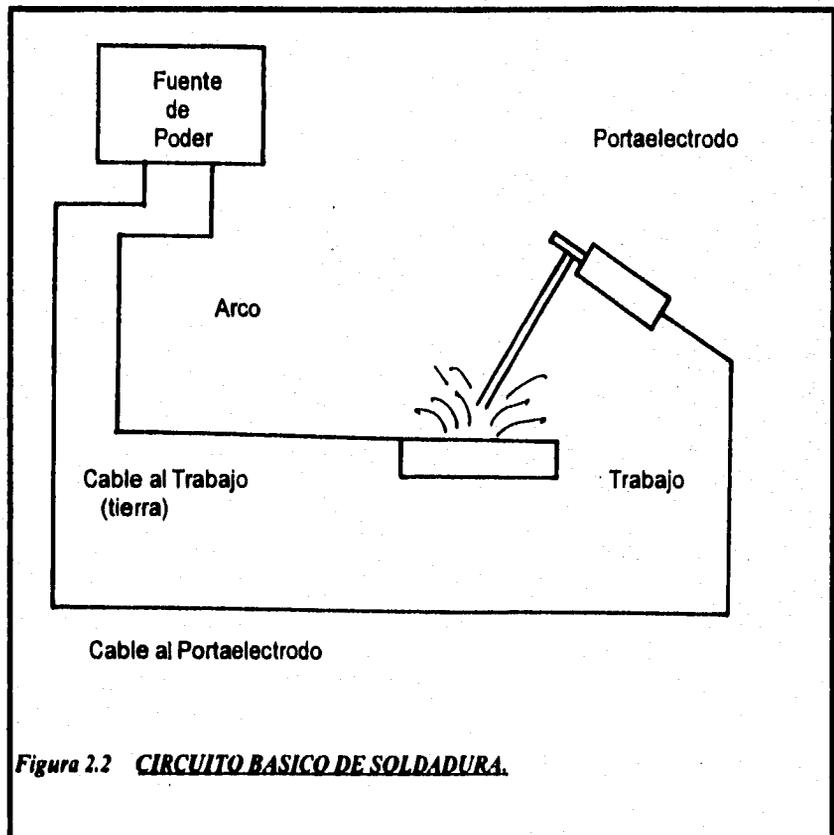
CIRCUITO BASICO DE SOLDADURA.
